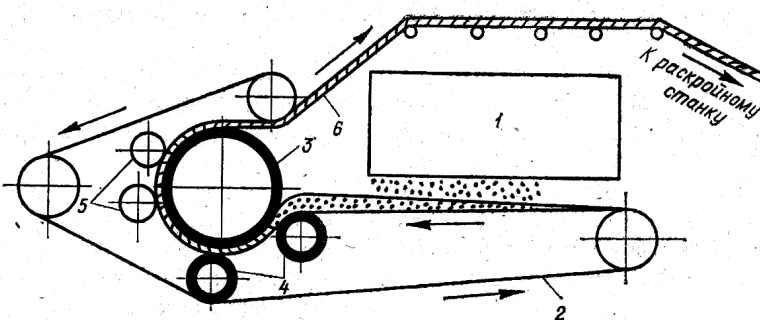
Схема линии с каландровым (валковым) прессом: 1 – формирующая машина; 2 – непрерывная стальная лента; 3 – главный обогреваемый барабан (каландр); 4 – прижимные обогреваемые барабаны; 5 – прижимные валики; 6 – готовая древесная плита
